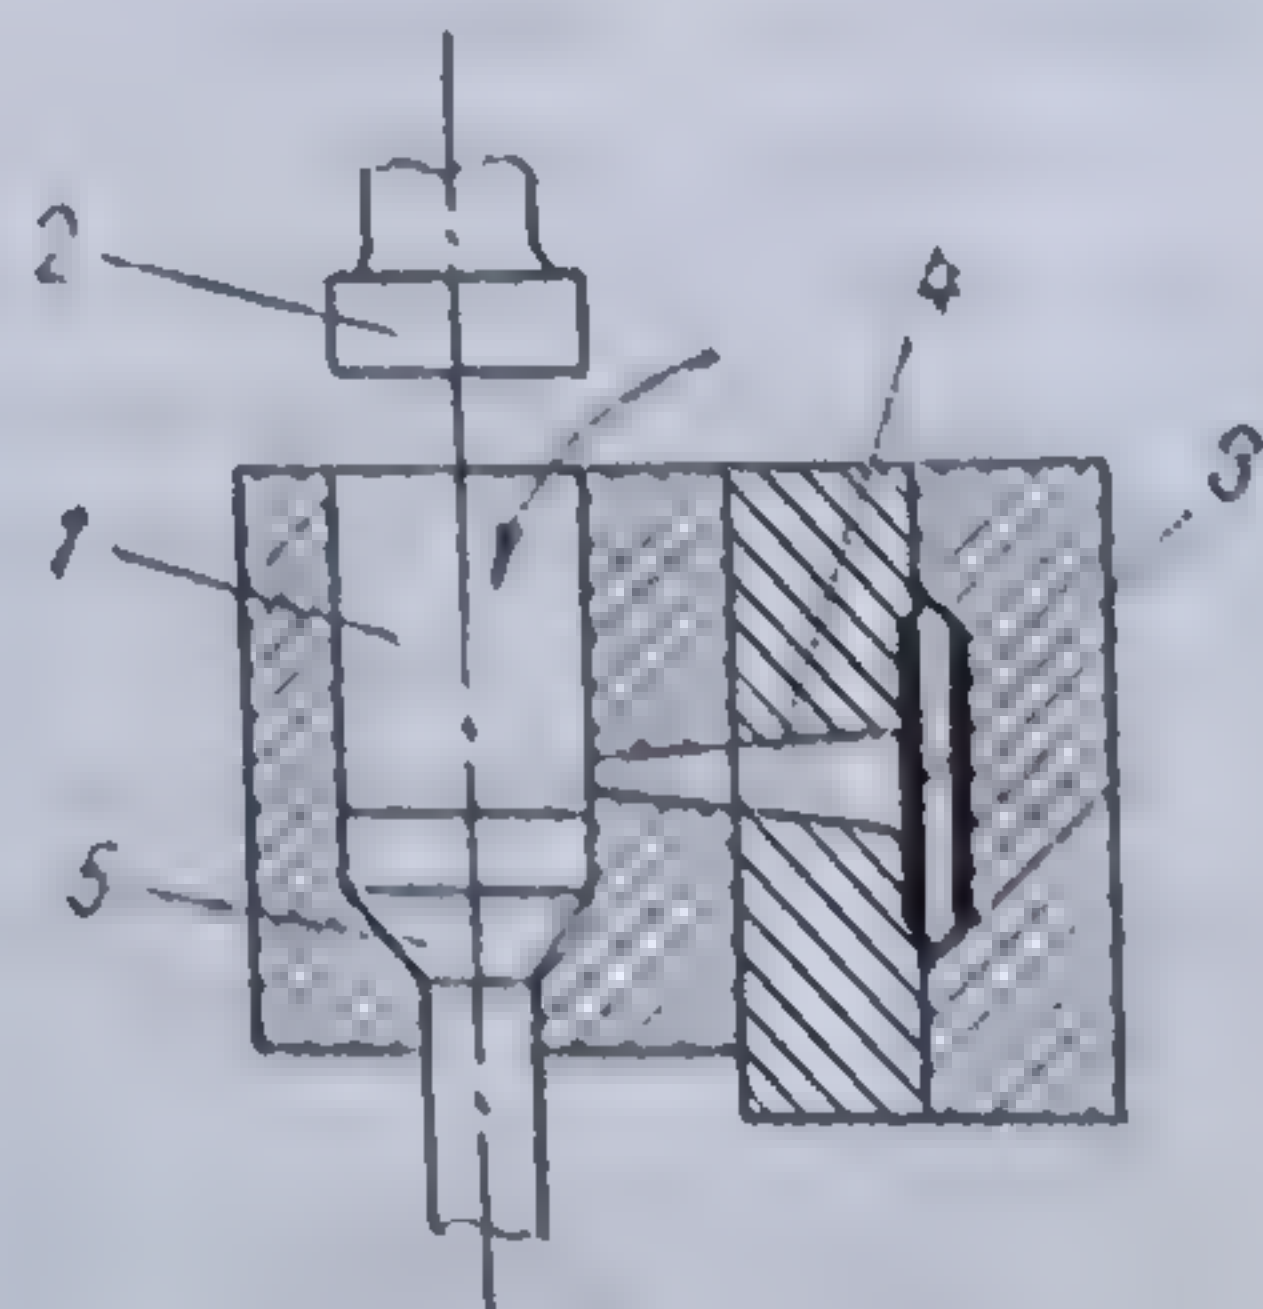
Cameră rece utilizată la mașinile pentru turnare sub presiune.
